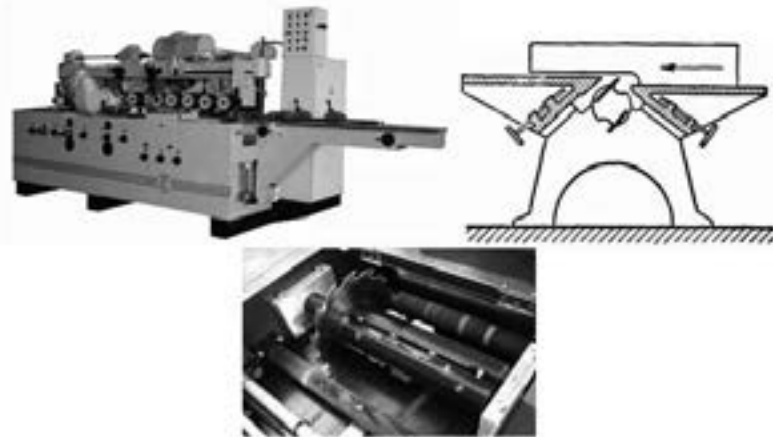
Стругальний верстат СР-12, схема стругання та ножова частина
